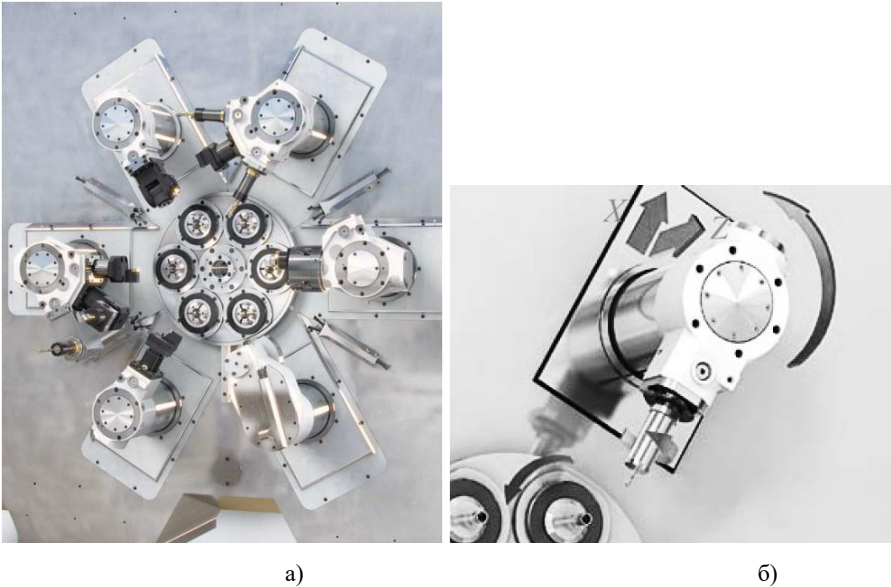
Інструментальні блоки: а – поперечні; б – поперечна каретка
